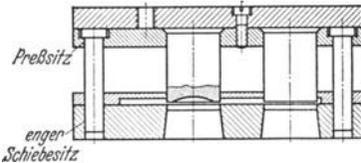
4faches Schnittwerkzeug mit Bolzenführung.
